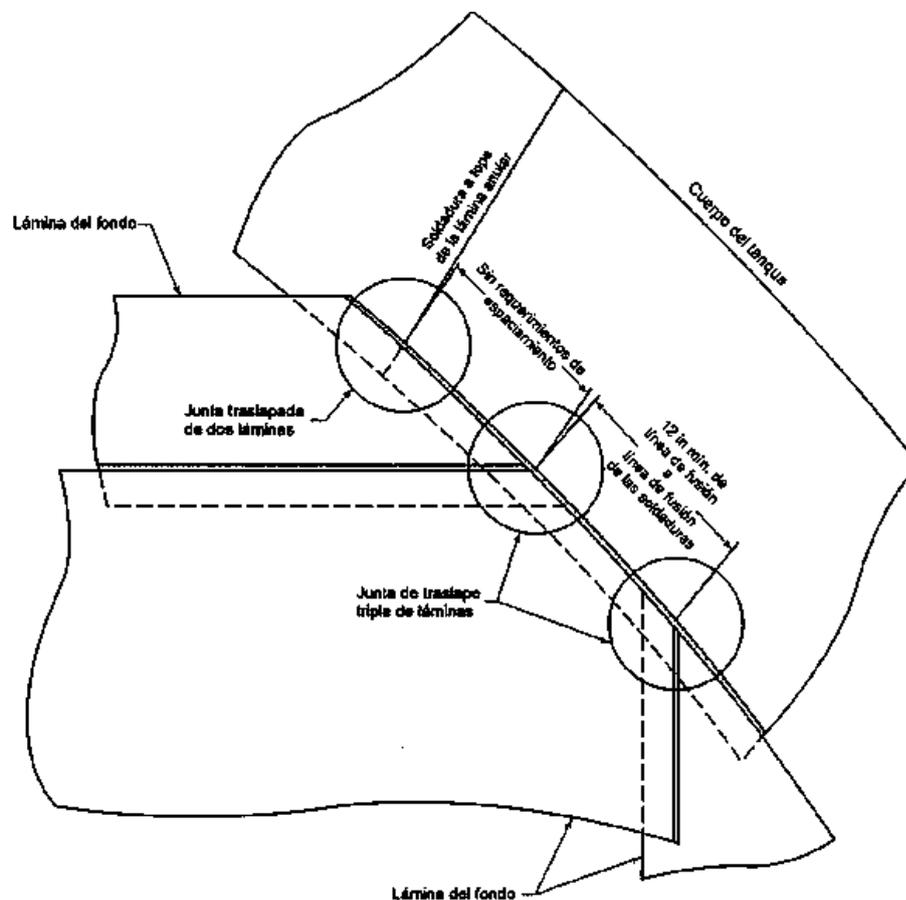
Espaciado de soldaduras de láminas triples en la lámina anular.
